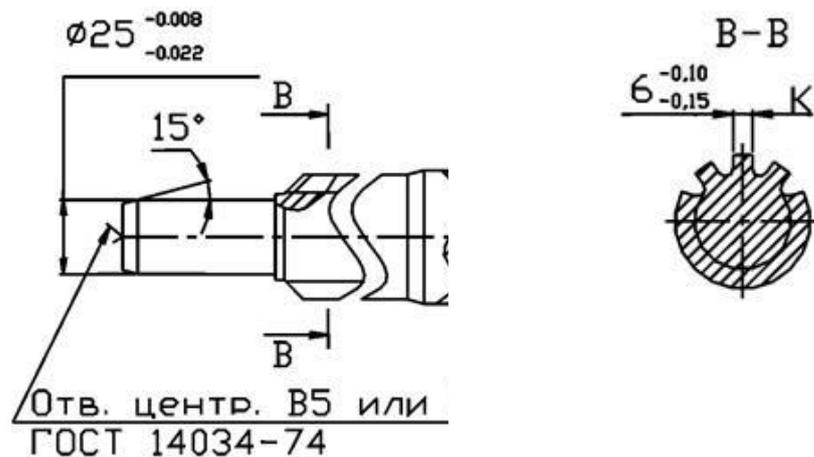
Предельные размеры зубьев шлица первичного вала коробки передач мод.14 автомобиля КамАЗ [2, 3]
